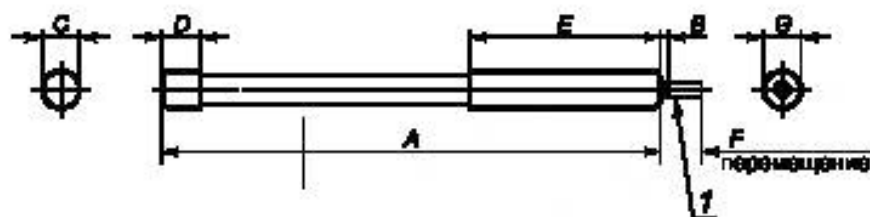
(IA) — Плавкие вставки со двоянным корпусом
